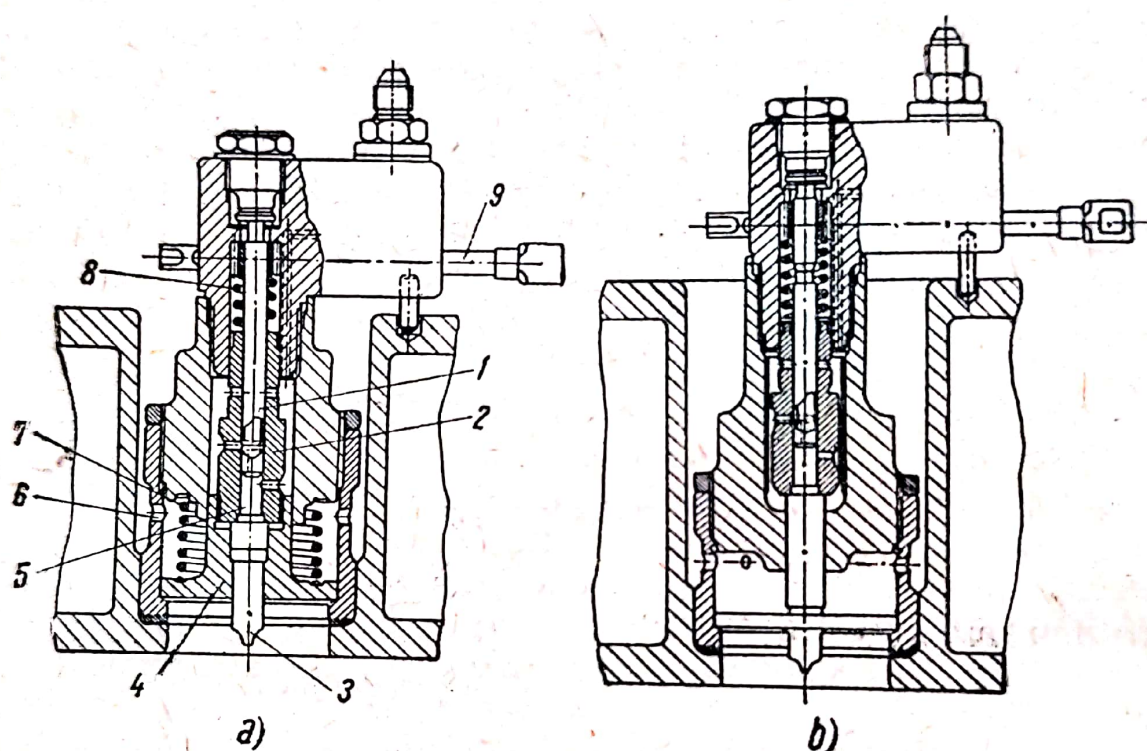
Sistem de injecție cu acțiune autopneumatică propus de prof. dr. Koşkin.
